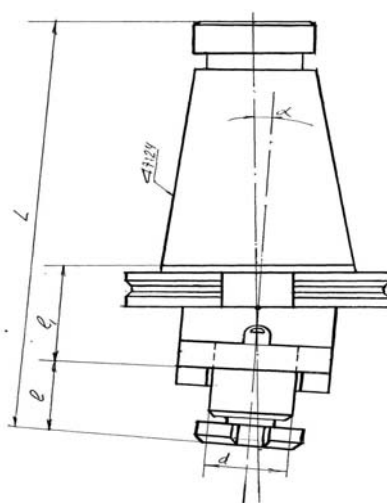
Ескіз спеціальної оправки для фрези-протяжки
